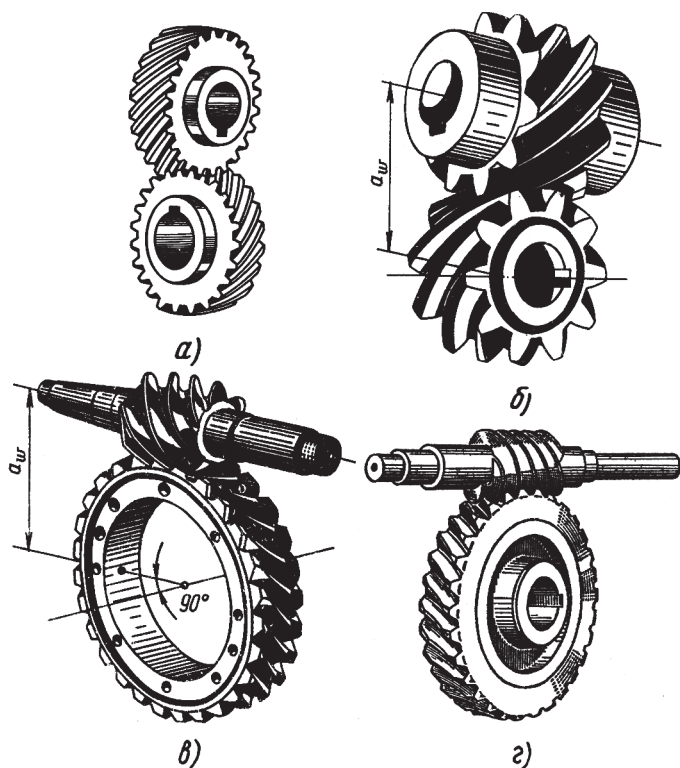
Зубчатые передачи с перекрещивающимися осями
